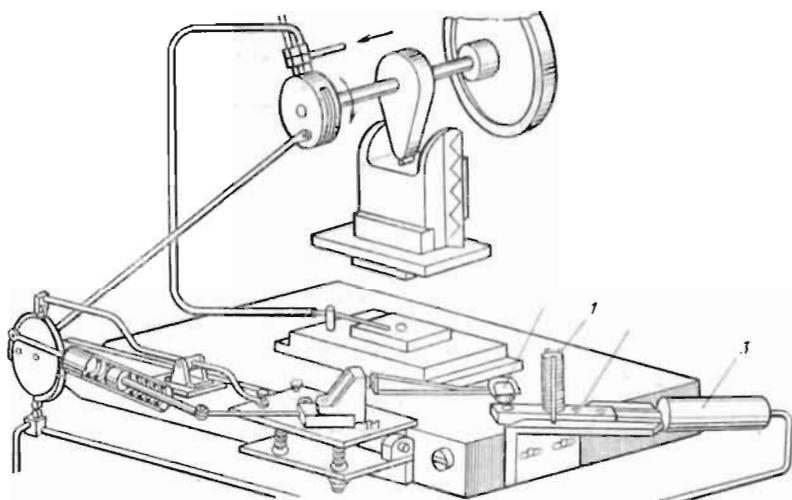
Схема механической руки для подачи в штамп заготовок из шиберного устройства:
